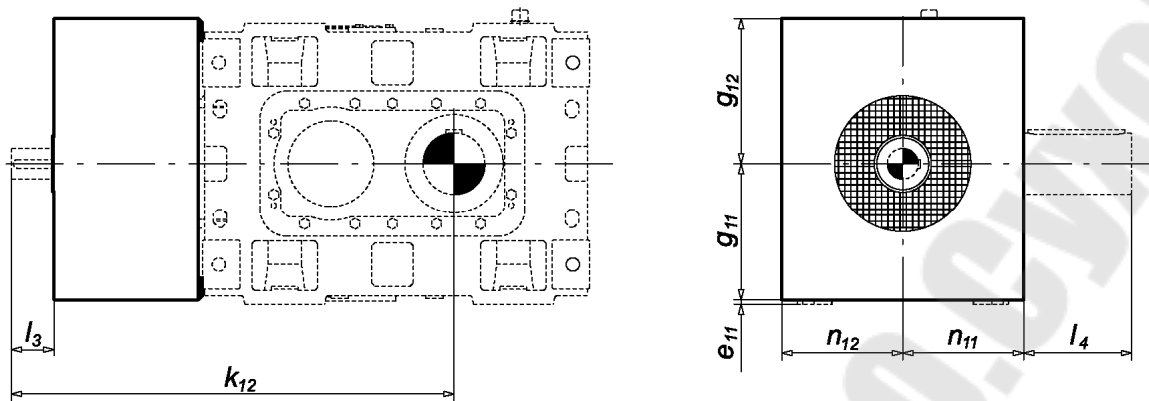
Вентиляторы для редукторов коническо–цилиндрических
